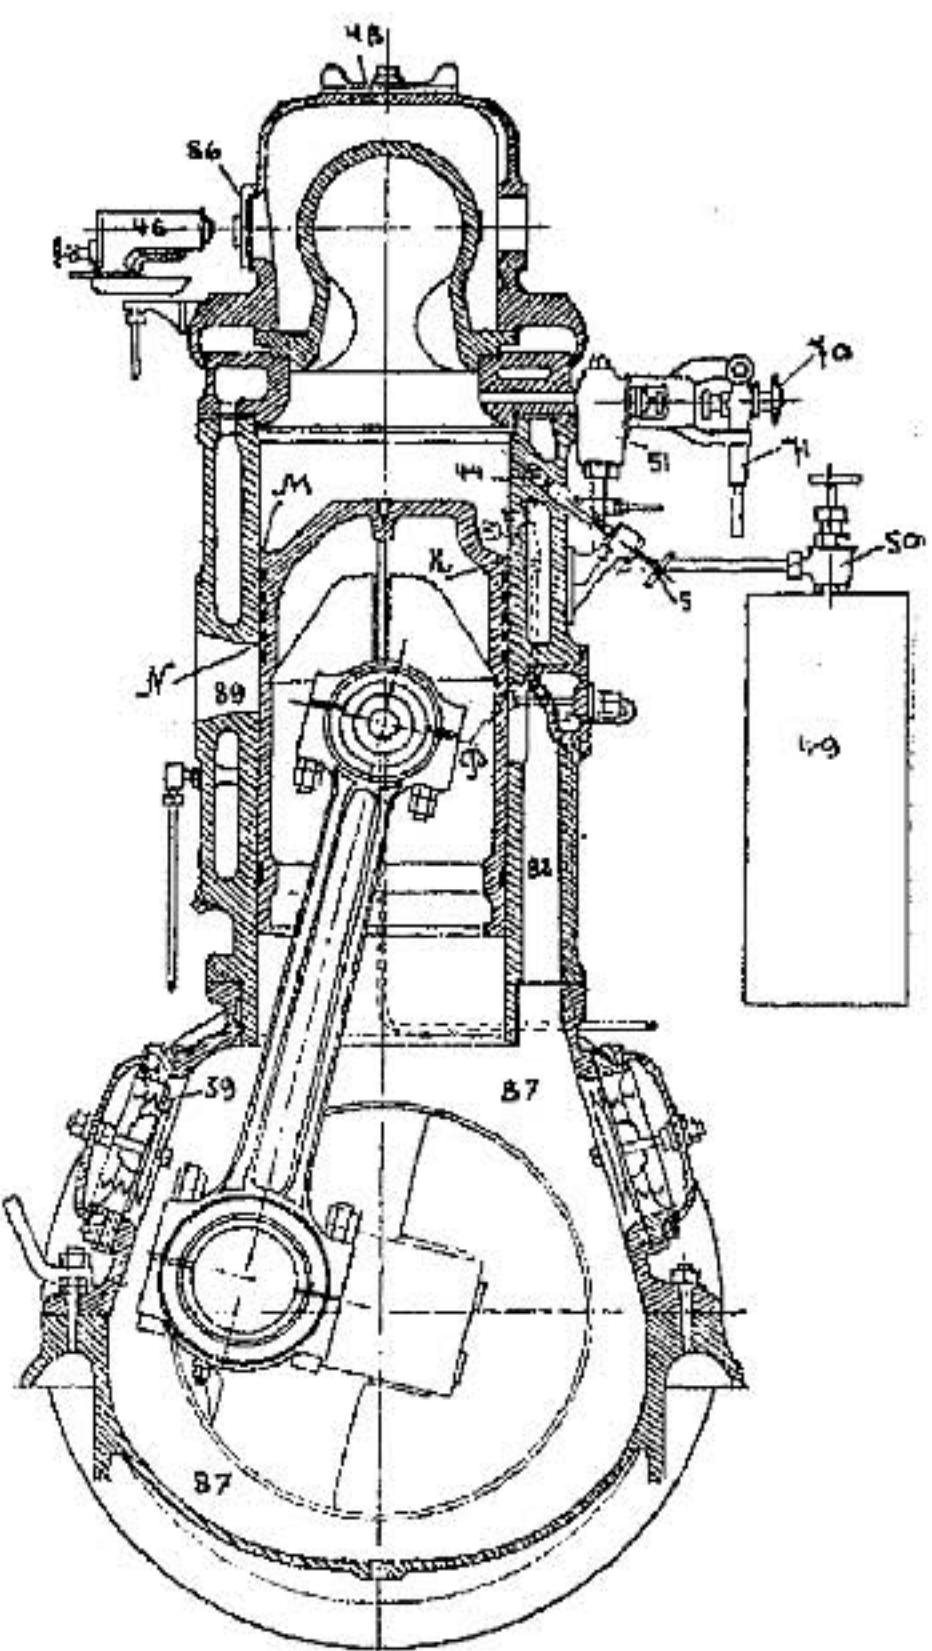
Поперечный разрезъ нефтяного двигателя Ижорского Завода.
